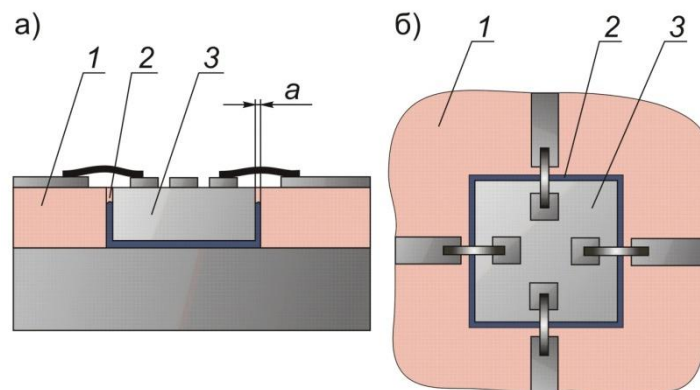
Монтаж бескорпусного кристалла на подложку в «окно» конструкционного фотополимера; а) разрез и б) вид сверху: 1 – подложка, 2 – углубление, 3 - кристалл
